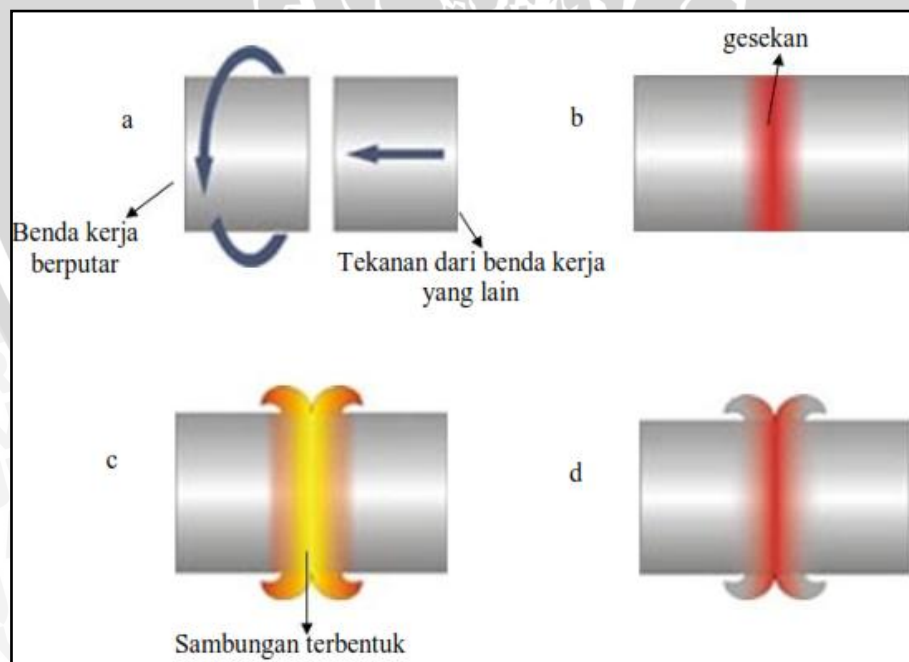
Mekanisme *Friction Stir Welding
